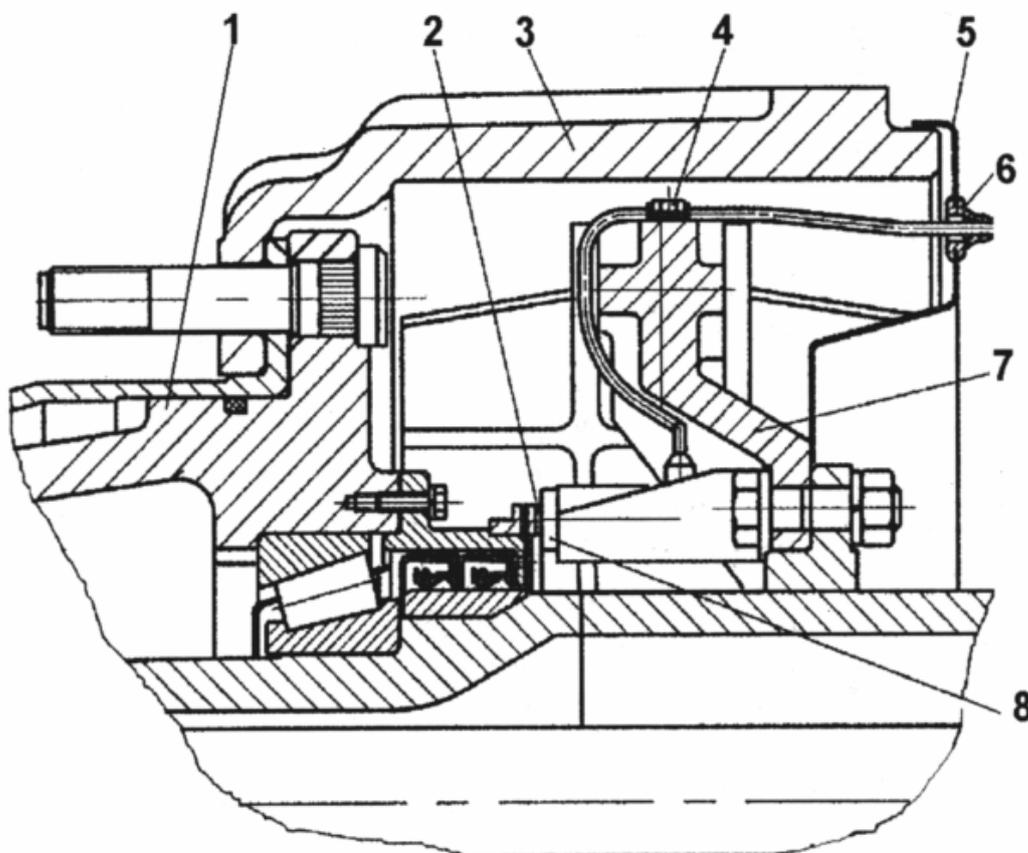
Установка датчика АБС в колесе ведущего моста: 1 – ступица; 2 – барабан тормозной; 3 – ротор датчика; 4 – скоба; 5 – щиток тормозного механизма; 6 – втулка провода; 7 – суппорт
